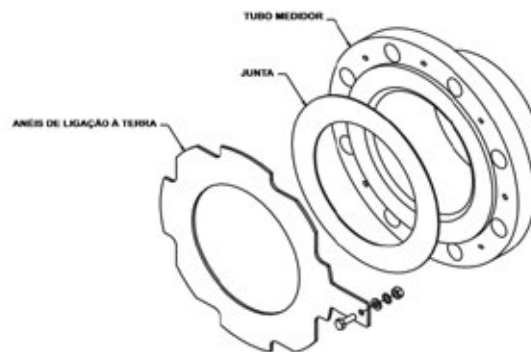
Exemplo de anel equipotencial e sua aplicação
